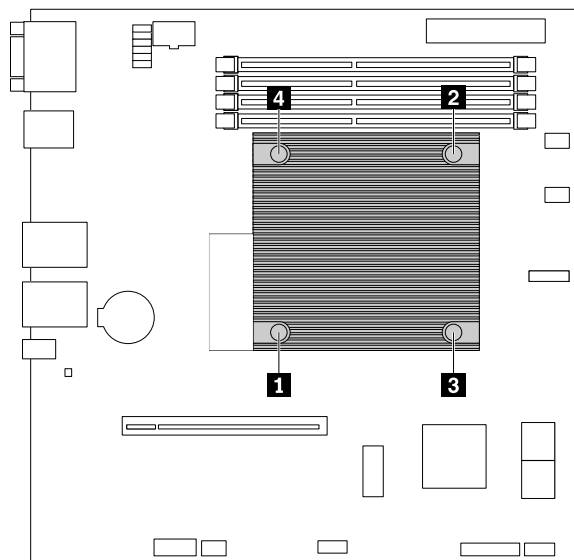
Befestigungsschrauben des Kühlkörpers anbringen
